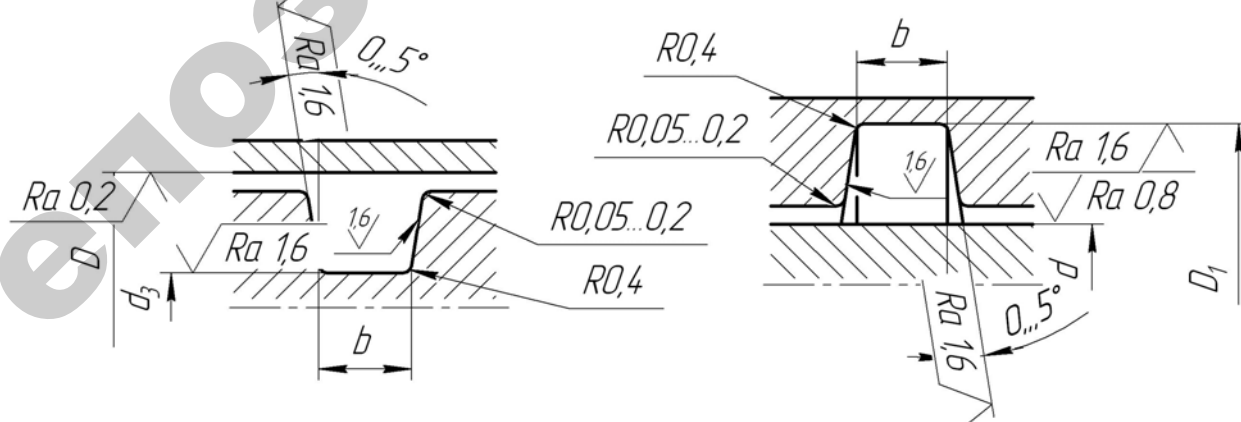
Канавки под резиновые уплотнительные кольца
